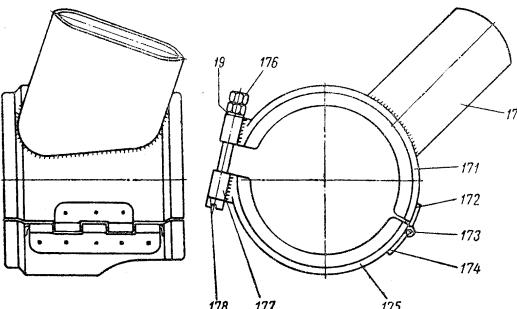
Корпус первой ступени (узел) АК150Н-12.
